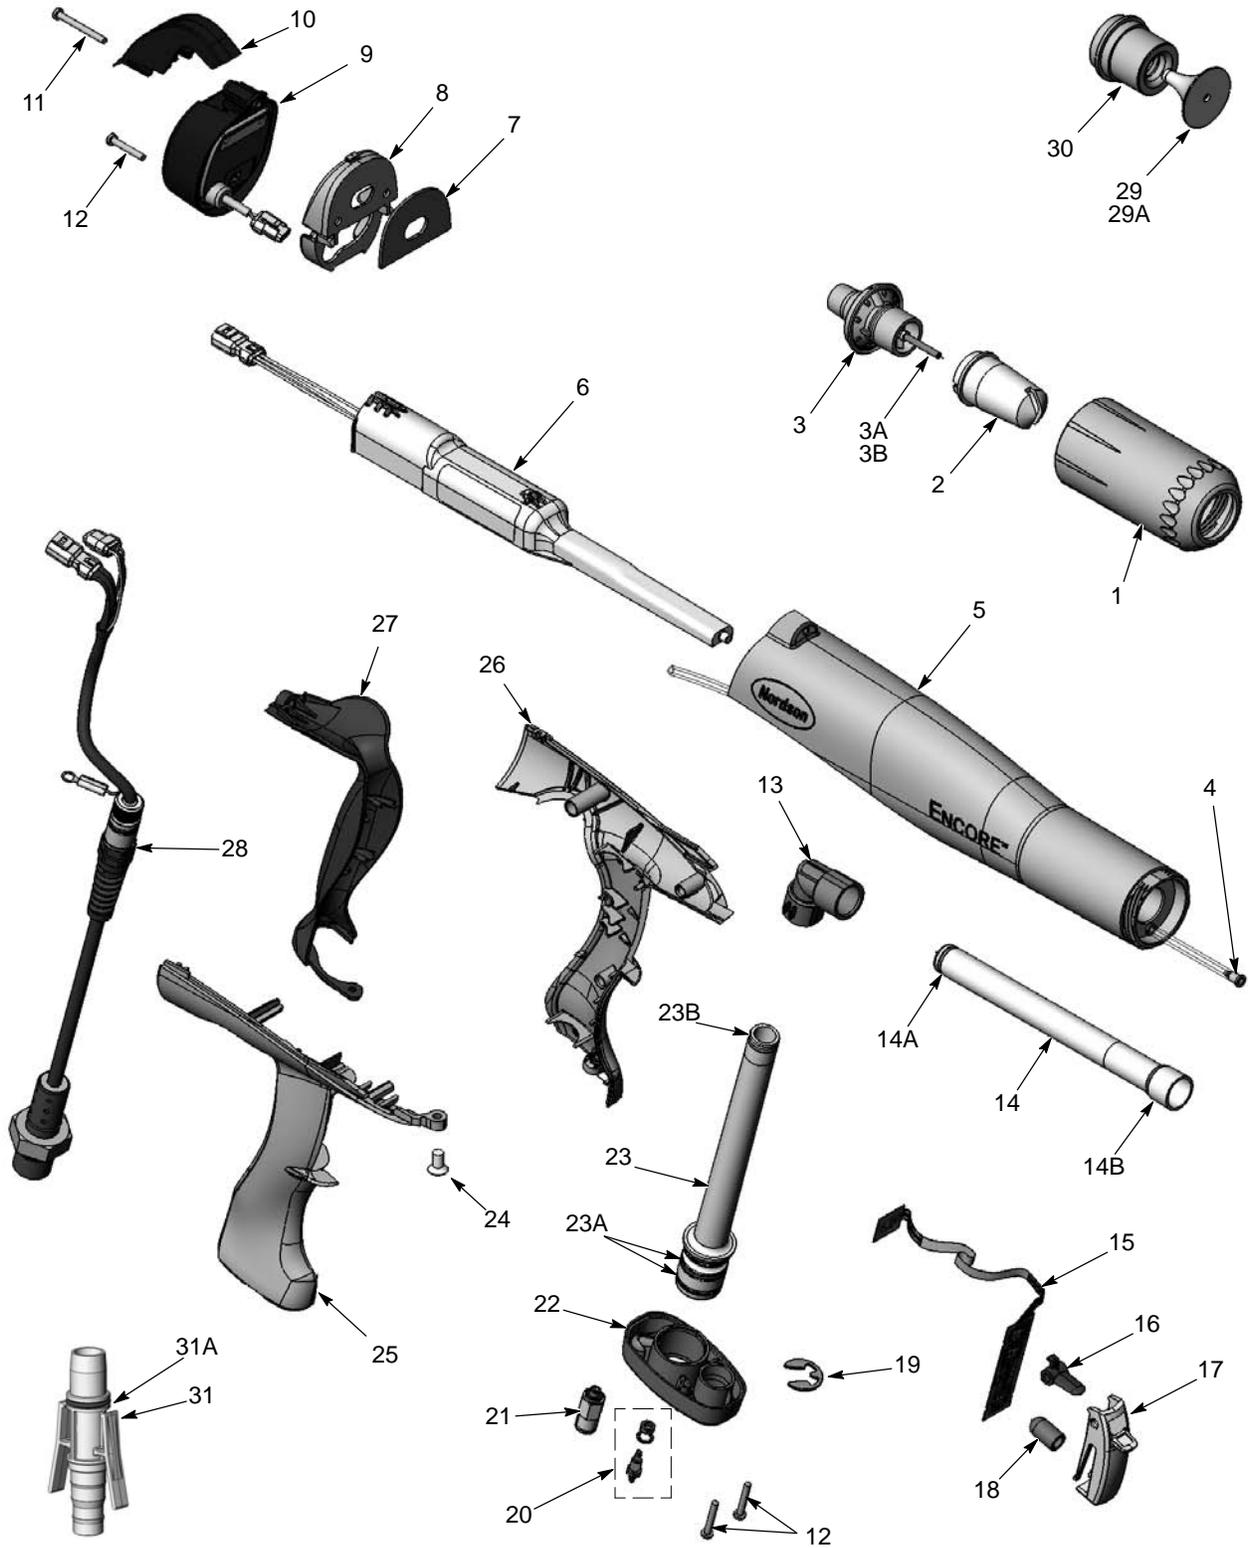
Vista despieceada de la pistola de aplicación manual Encore y accesorios
